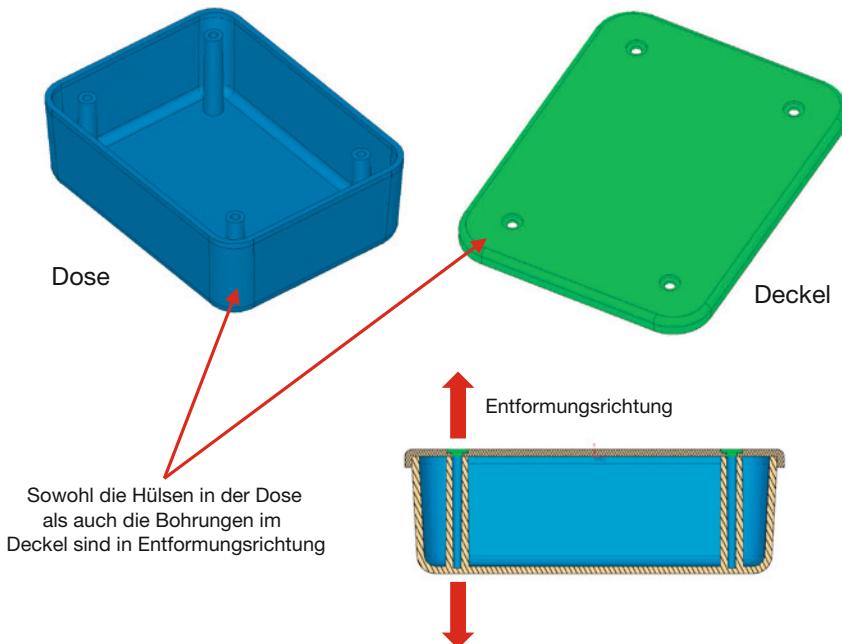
Teile für Auf-Zu-Werkzeug
